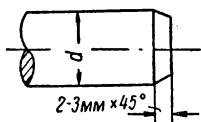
Вид конца заготовки стержня под нарезание резьбы плашками.
